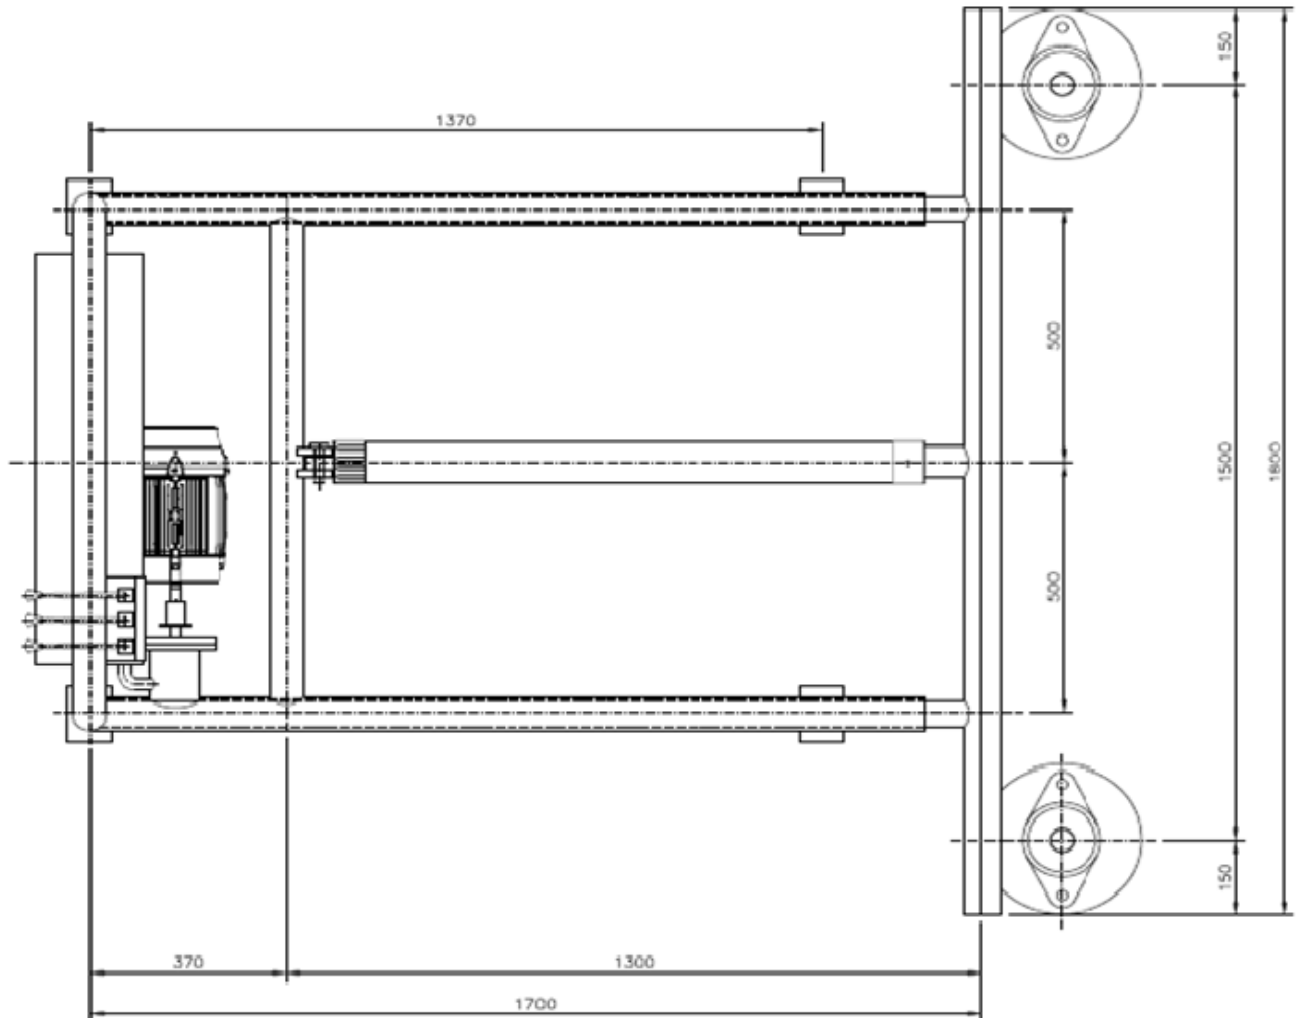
Dispositivo para Elevação, Vista superior. Escala 1:5, 2014.
